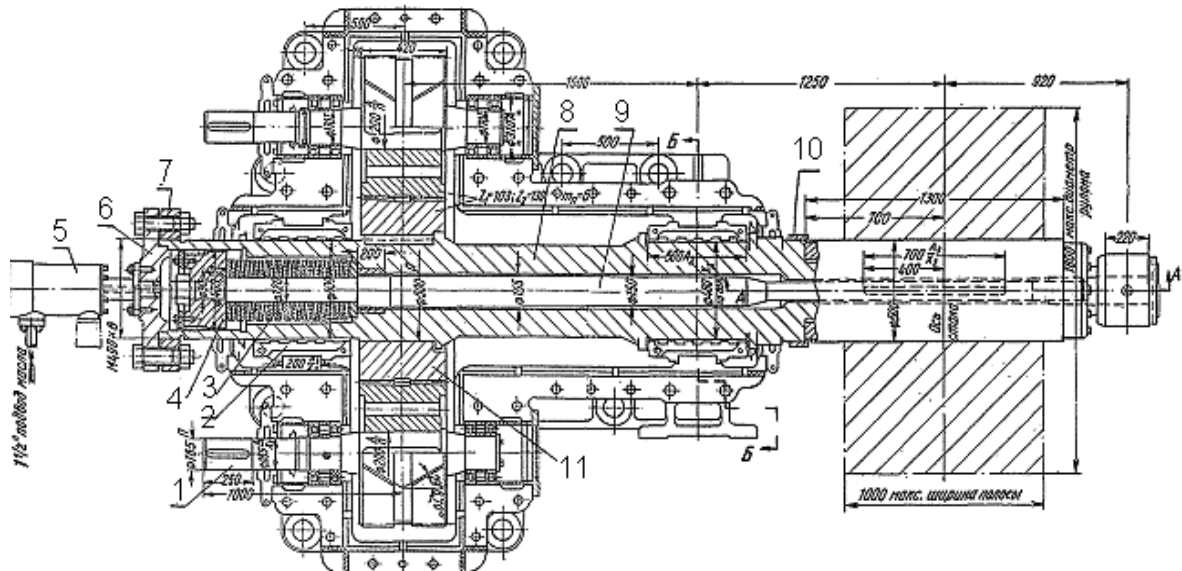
Моталка реверсивного стану 1200: 1 – вал з шестернею; 2 – вкладиш-залівка; 3 – пружина; 4 – поршень; 5 – вертлюжок для підводу мастила; 6 – кришка; 7 – фланець; 8 – вал барабану; 9 – шток; 10 – кільце; 11 – зубчате колесо.
